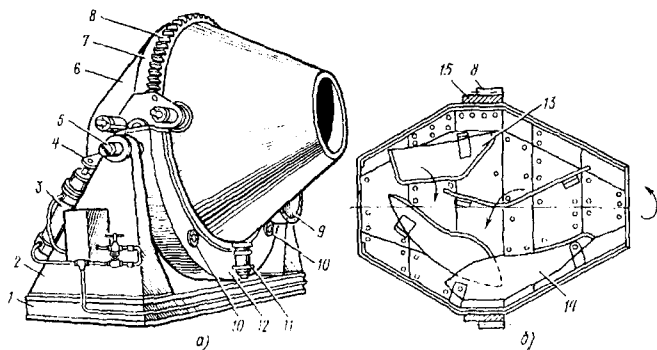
Бетоносмеситель с двухконусным барабаном: а - общий вид; б - схема устройства смесительного барабана; 1 - станина; 2 - стойка; 3 - пневмоцилиндр; 4 - кронштейн; 5 - шип траверсы; 6 - барабан; 7 - обод; 8 - зубчатый венец; 9 - электродвигатель; 10 - опорные ролики; 11 - упорный ролик; 12 - траверса; 13, 14 - лопасти; 15 - цилиндрическая вставка.
